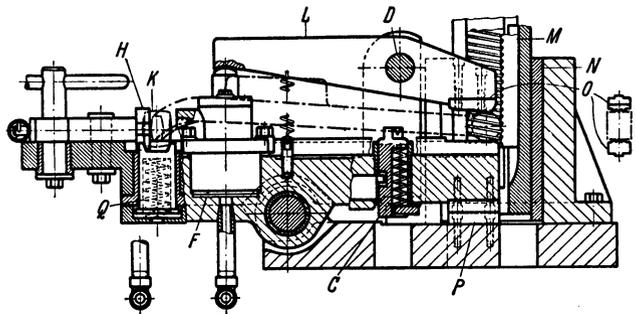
Seitenansicht der Vorrichtung Abb. 85.
